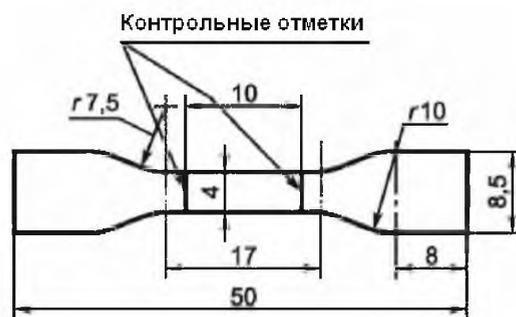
Образец в виде двусторонней лопатки с меньшими размерами
